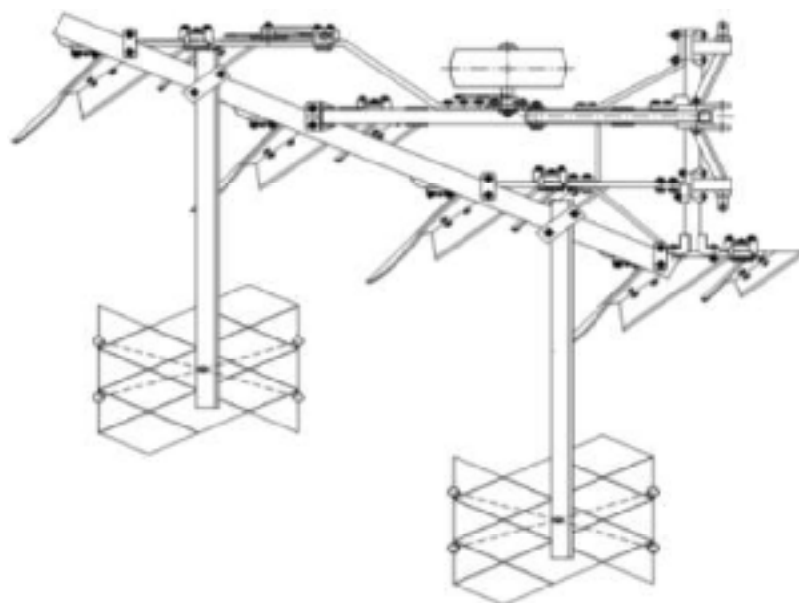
Комбинированный пахотный агрегат с навесными зубвыми боронами
